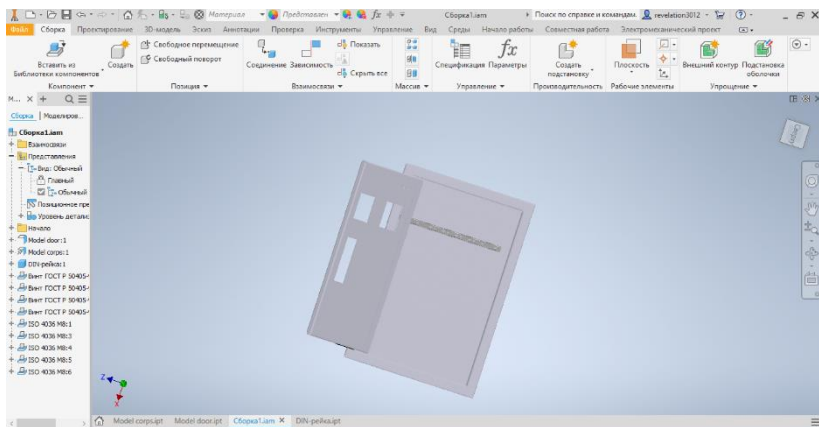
Готова 3D модель щита з DIN-рейкою
